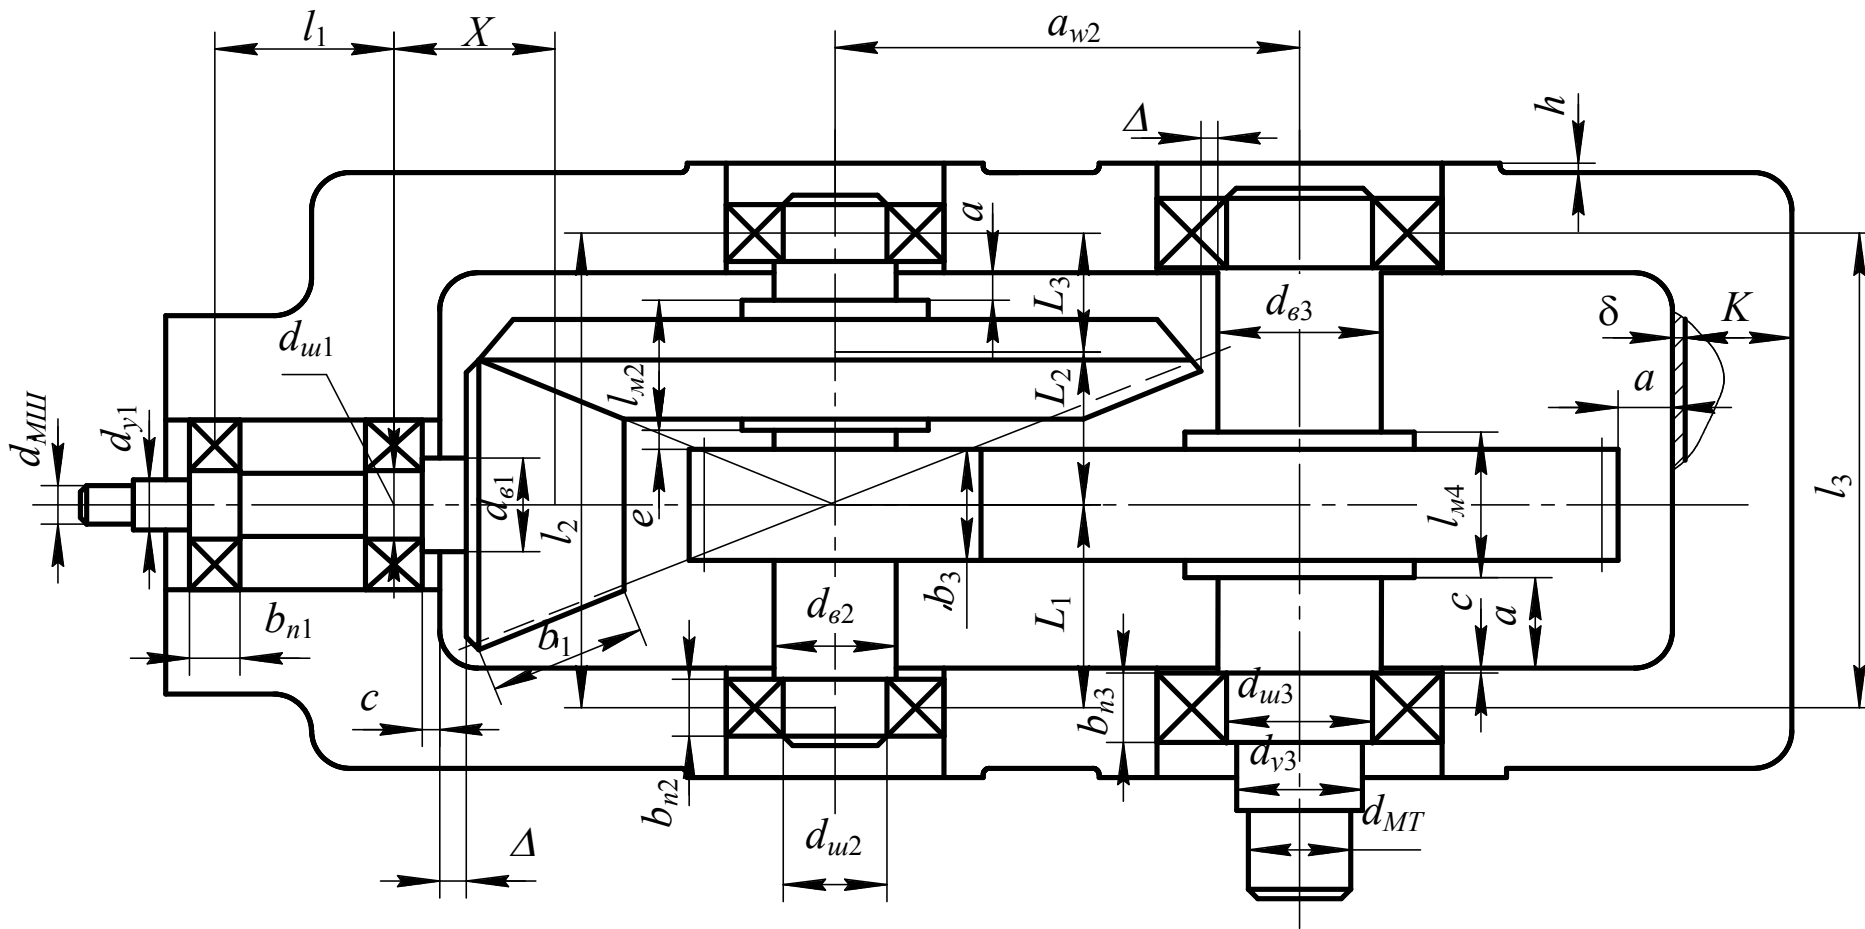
Эскизная компоновка двухступенчатого коническо-цилиндрического редуктора
